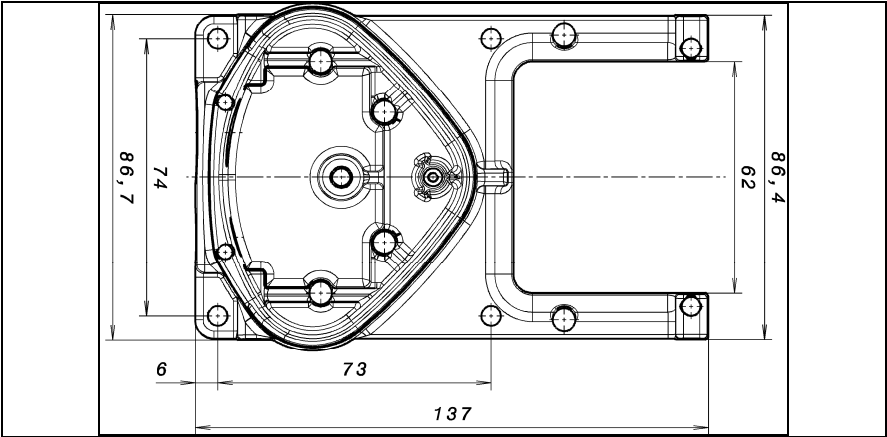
Bohrbild Standard-Wand- Adapterplatte BG A
